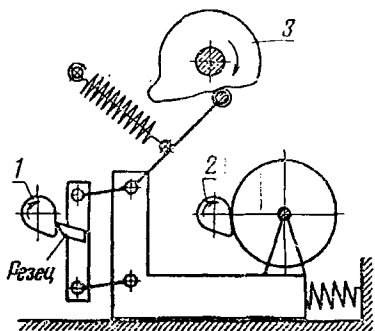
Принципова схема обточування кулачка розподільного валу на токарно-копіювальному верстаті: 1 – заготовка; 2 – копіювальний вал; 3 – копір.
